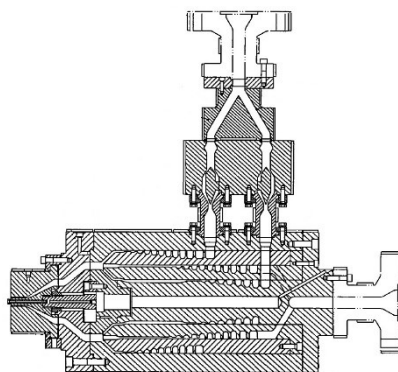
Головка для формування тришарової трубчастої заготовки (пат. № CN201253946Y)
